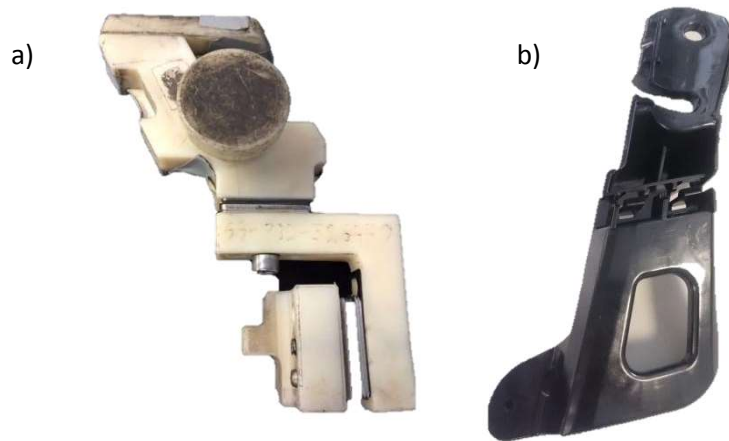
a) Dispositivo de apoyo para montaje de guía de fascia.
